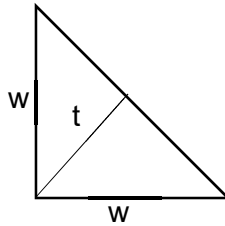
Dimensiones de una soldadura de filete.
